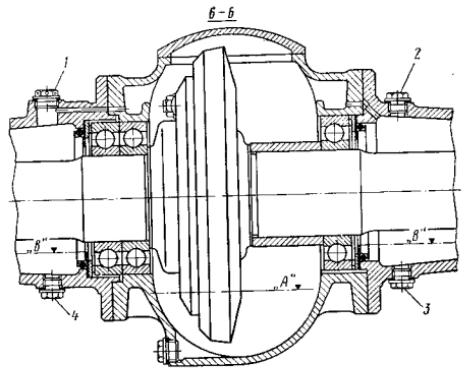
Двухступенчатый редуктор (разрез по Б-Б, см. рис. 18):
